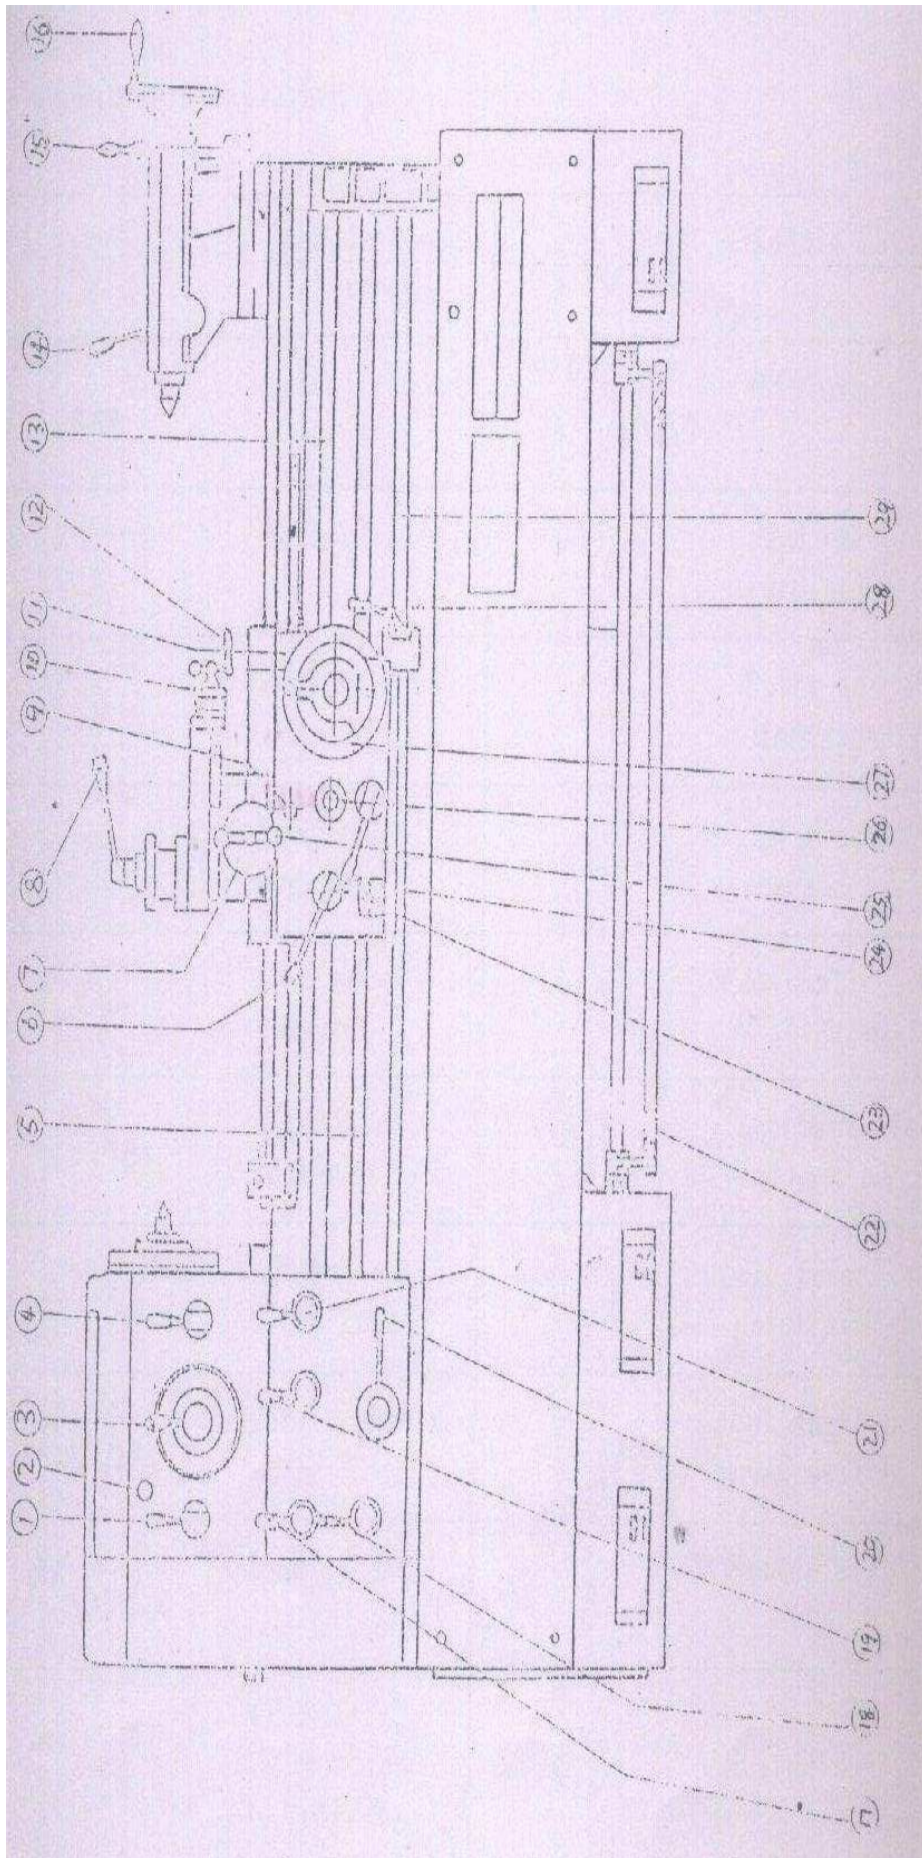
Внешний вид и рычаги управления токарного станка
